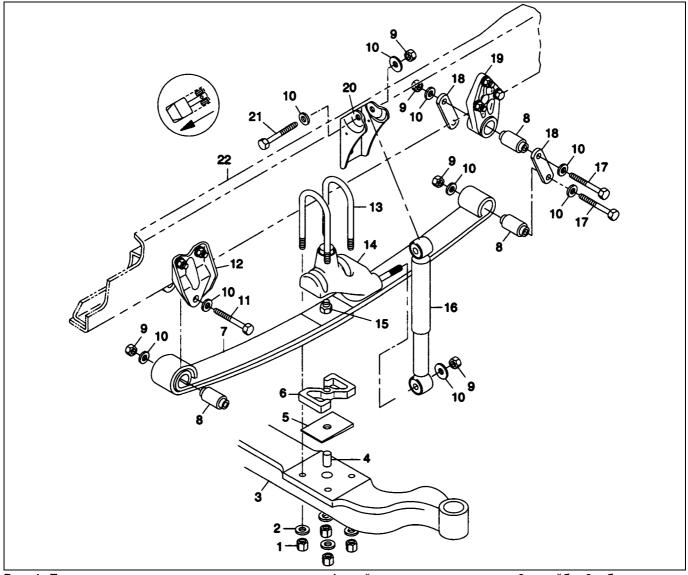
Передняя подвеска с резиновыми втулками. 1 - гайка стремянки рессоры, 2 - шайба, 3 - балка моста, 4 - штифт, 5 - проставка (клин) регулировки продольного наклона шкворня, 6 - прокладка, 7 - рессора в сборе, 8 - резиновая втулка, 9 - контргайка (3/4"-10), 10 - закаленная шайба, 11 - болт ушка рессоры, 12 - передний кронштейн рессоры, 13 - стремянка, 14 - ограничитель хода подвески и нижняя опора амортизатора, 15 - центральный болт рессоры, 16 - амортизатор, 17 - болт серьги (3/4"-10), 18 - серьга рессоры, 19 - кронштейн серьги, 20 - верхняя опора амортизатора, 21 - болт (3/4"-10), 22 - лонжерон рамы.
